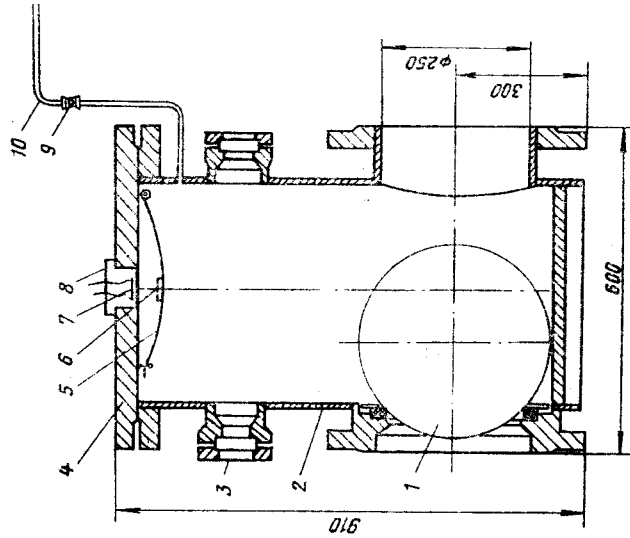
Поплавковый клапан (черт. НС 50.000, ВНИИПО):
